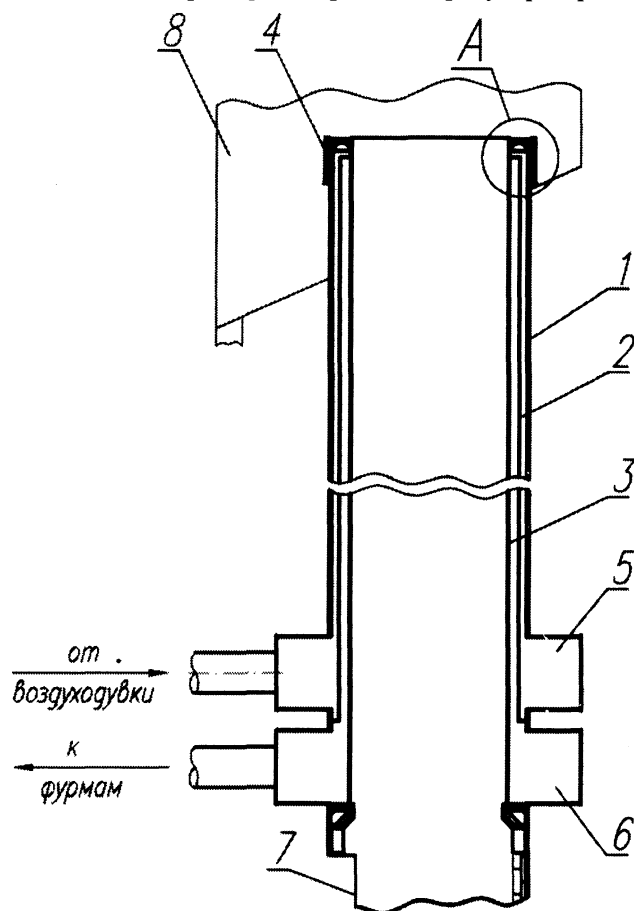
Схема рекуператора: 1 – корпус вагранки; 2 – средний (промежуточный) цилиндр; 3 – внутренний теплопринимающий корпус; 4 – компенсатор; 5 – коллектор холодного воздуха; 6 – коллектор горячего воздуха; 7 – загрузочное окно; 8 – пылеуловитель
